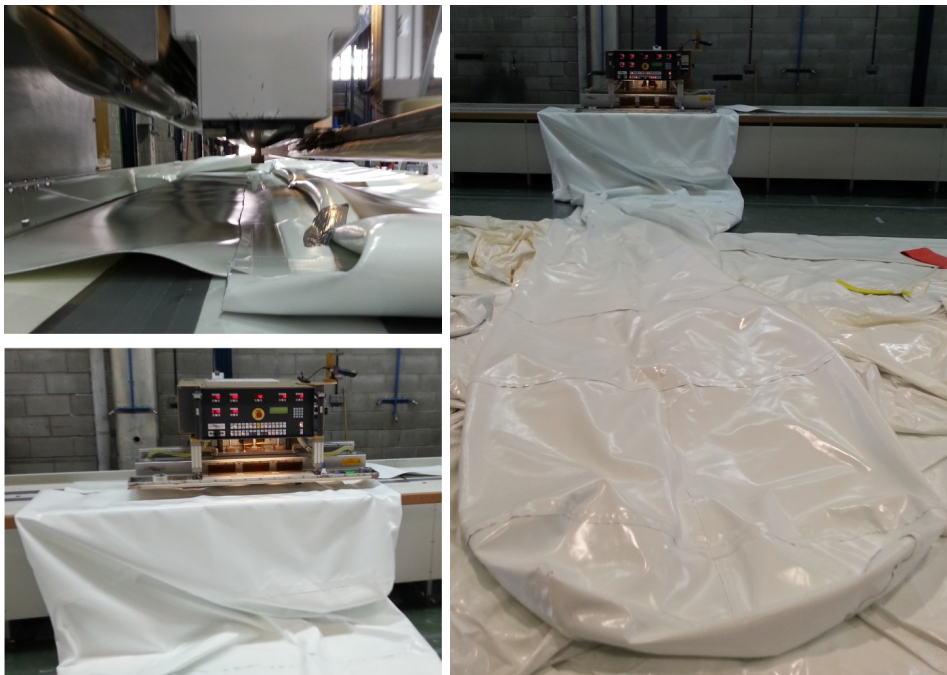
Soldadura del cuerpo central de la cámara exterior del tubo hinchable
